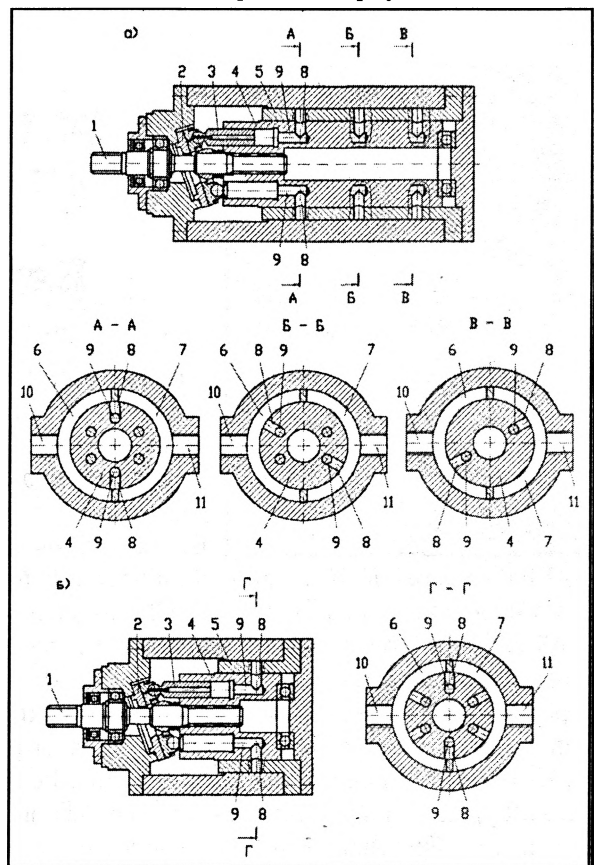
Аксиально-поршневая гидромашин с полукольцевыми пазами на образующей поверхности подшипника скольжения: 1 — ведущий вал; 2 — наклонная шайба; 3 — поршень; 4 — блок цилиндров; 5 — подшипник скольжения; 6, 1 — полукольцевые пазы; 8, 9 — каналы блока цилиндров; 10, 11 — каналы корпуса гидромашин
